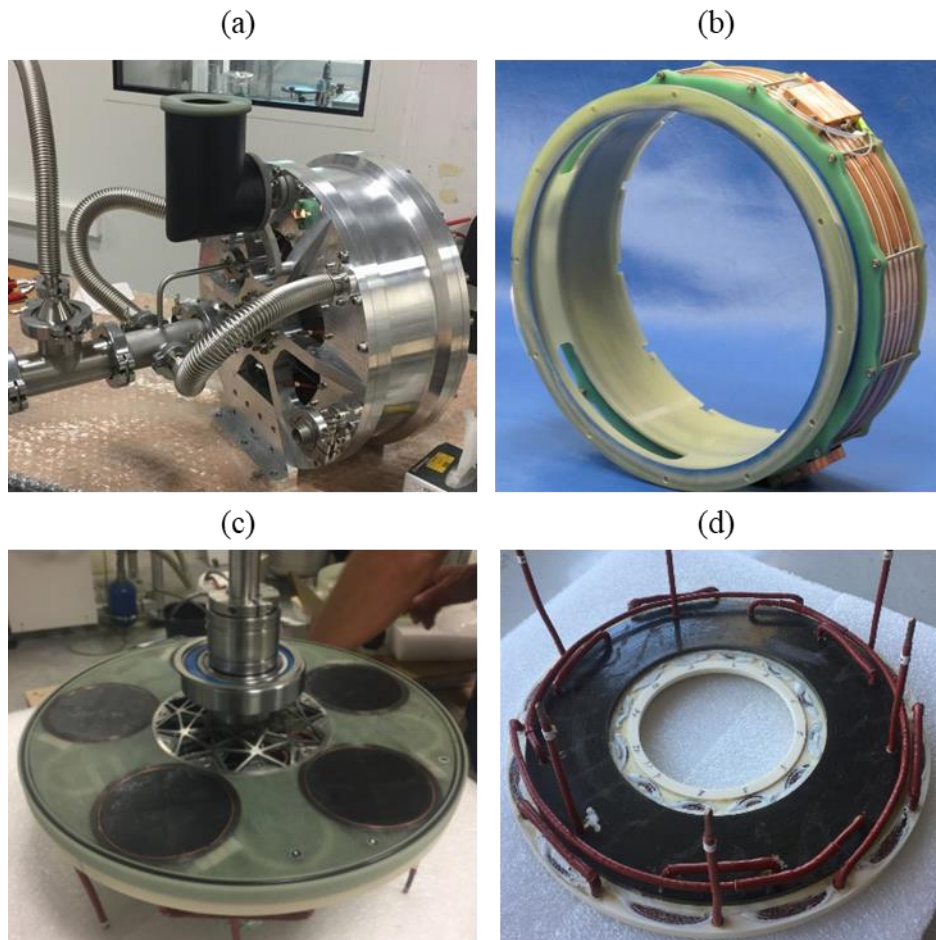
Prototypage de machine à modulation de flux axiale 50 kW. (a) Photographie de la machine. (b) Bobine supraconductrice Bi-2223. (c) Rotor comprenant 5 pastilles YBaCuO. (d) Induit cuivre.
